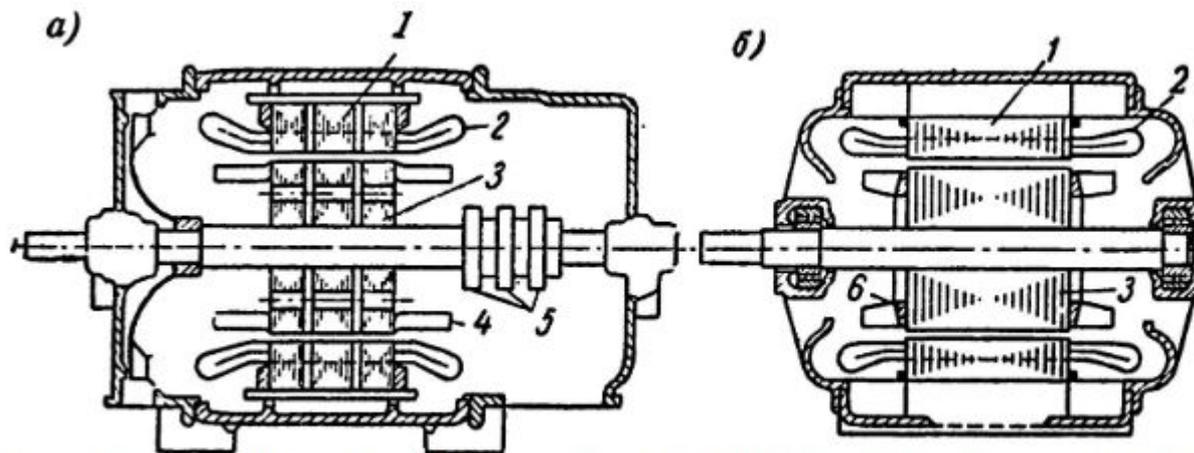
Конструктивная схема трехфазного асинхронного двигателя: а — с фазной обмоткой ротора, б — с короткозамкнутой обмоткой ротора
